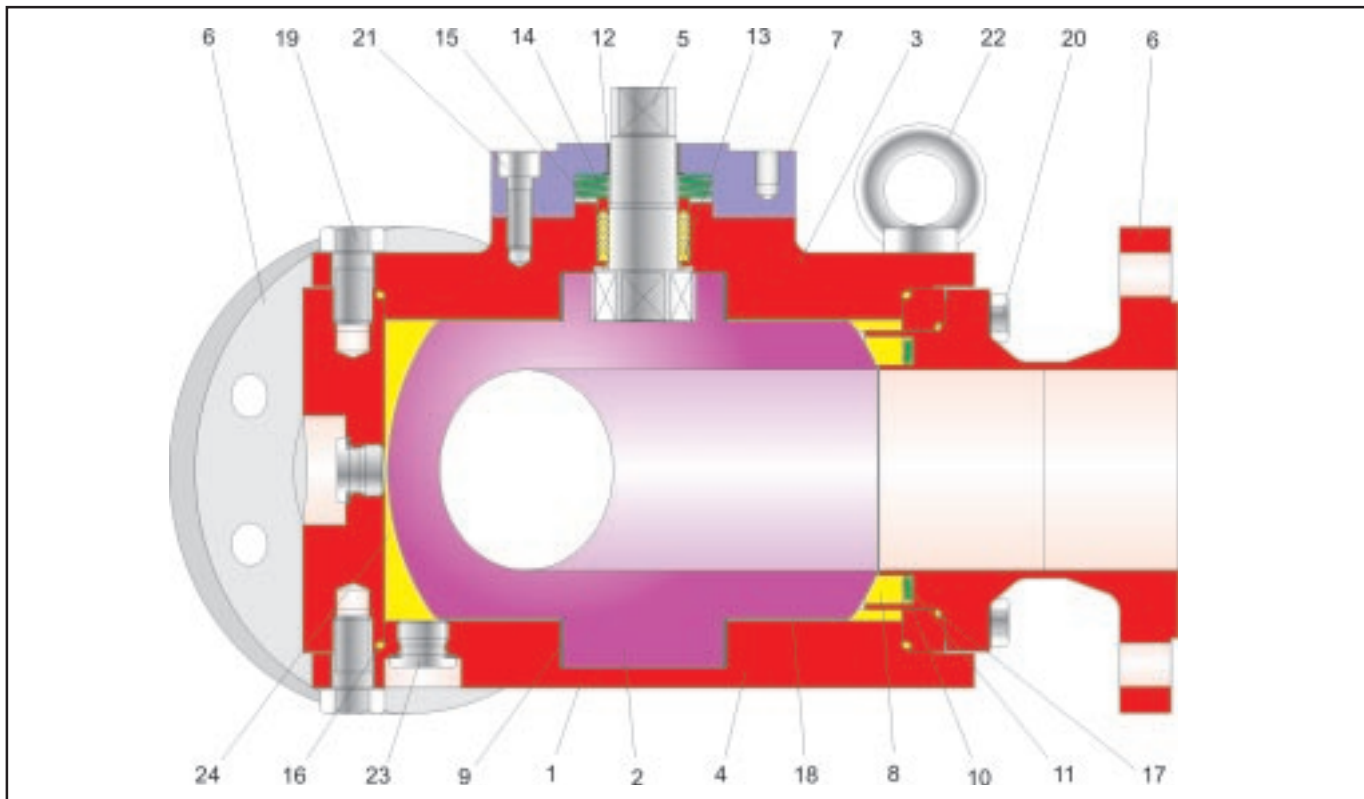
Schnittzeichnung der 3-Wege Molchweiche BR 29a
